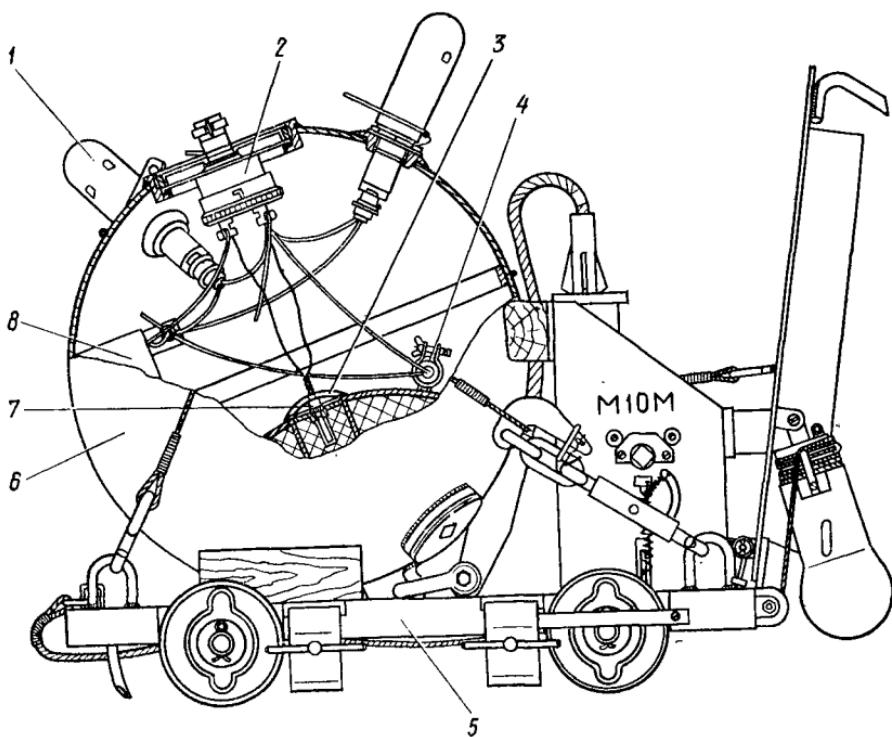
Мина ПДМ-ЗЯ (вид сбоку с разрезом корпуса):
